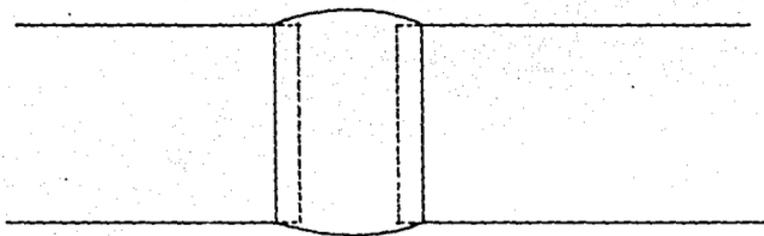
Soldadura con Ranura Rectangular
